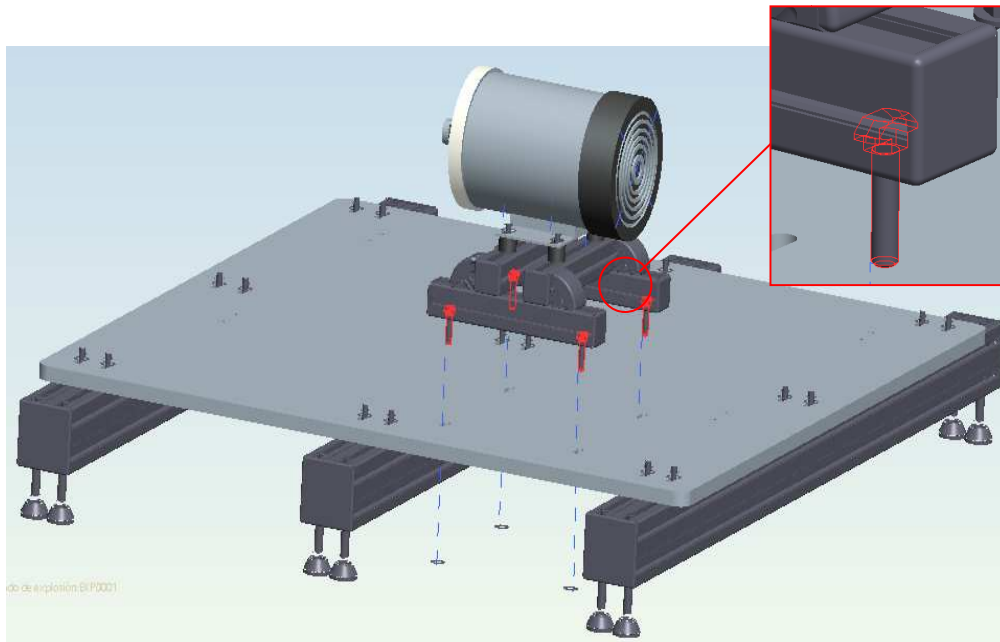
Explosionado de la unión bancada-apoyo motor
